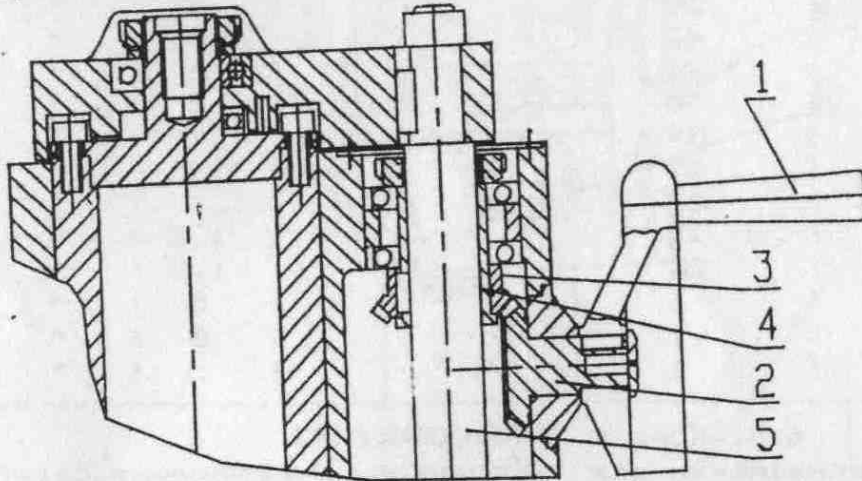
Механизм перемещения сверлильно-фрезерной головки
